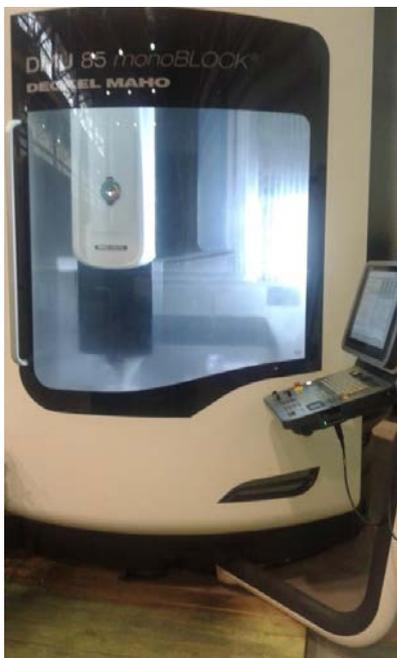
Обрабатывающий центр DMU 85 monoBLOCK
